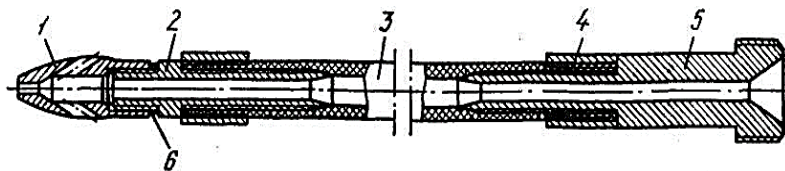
Конструкция шланга с головкой: 1 – головка; 2, 5 – штуцеры; 3 – шланг; 4 – кольцо; 6 – прокладка
